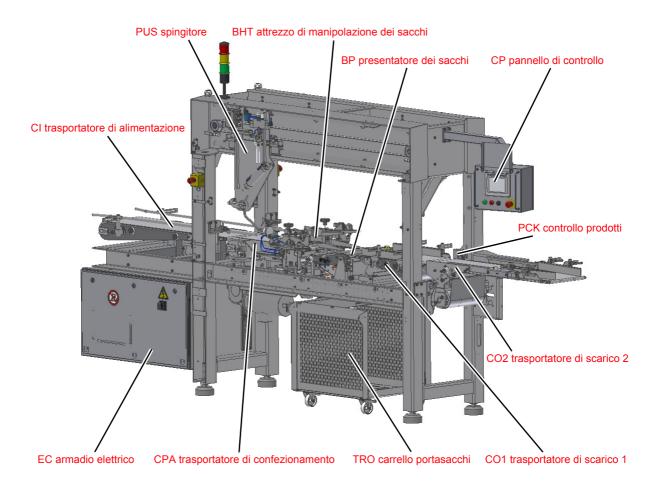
, Elementi principali della macchina (mostrati senza i ripari)
